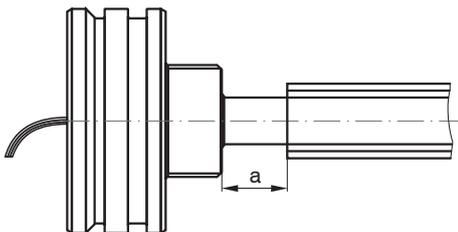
Position point zéro du tube de mesure, EDS- ... -Z
